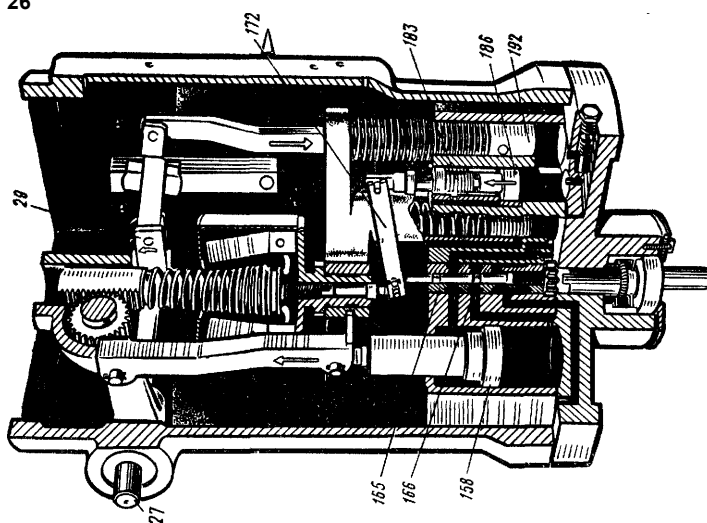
27 — выходной вал; 29 — рычаг изодрома; 158 — поршень сервомотора; 165 — распределительный золотник; 166 — втулка распределительного золотника; 172 — плавающий рычаг; 183 — пружина изодрома; 186 — принимающий поршень изодрома; 192 — задающий поршень изодрома
